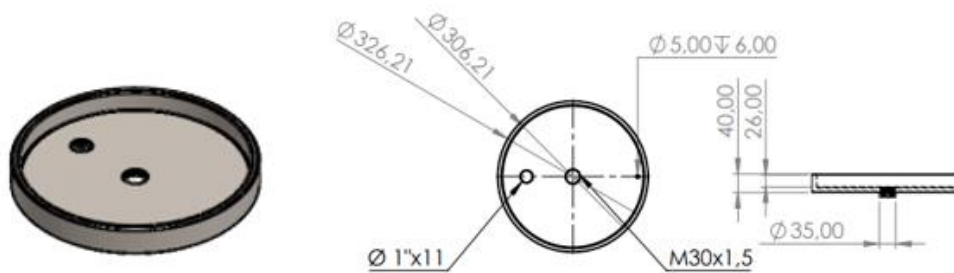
Dimensiones y Diseño de la tapa de la tolva. (Fuente Propia)
